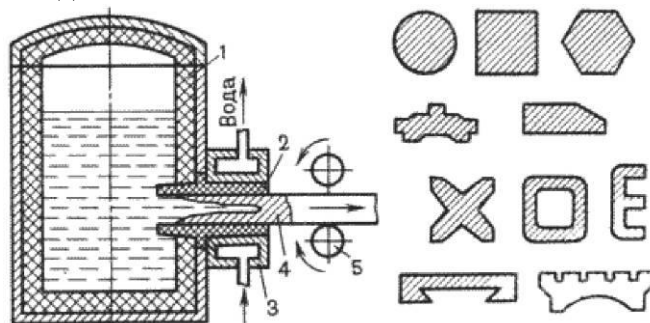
Схема непрерывного литья (а) и разновидности получаемых отливок (б)
